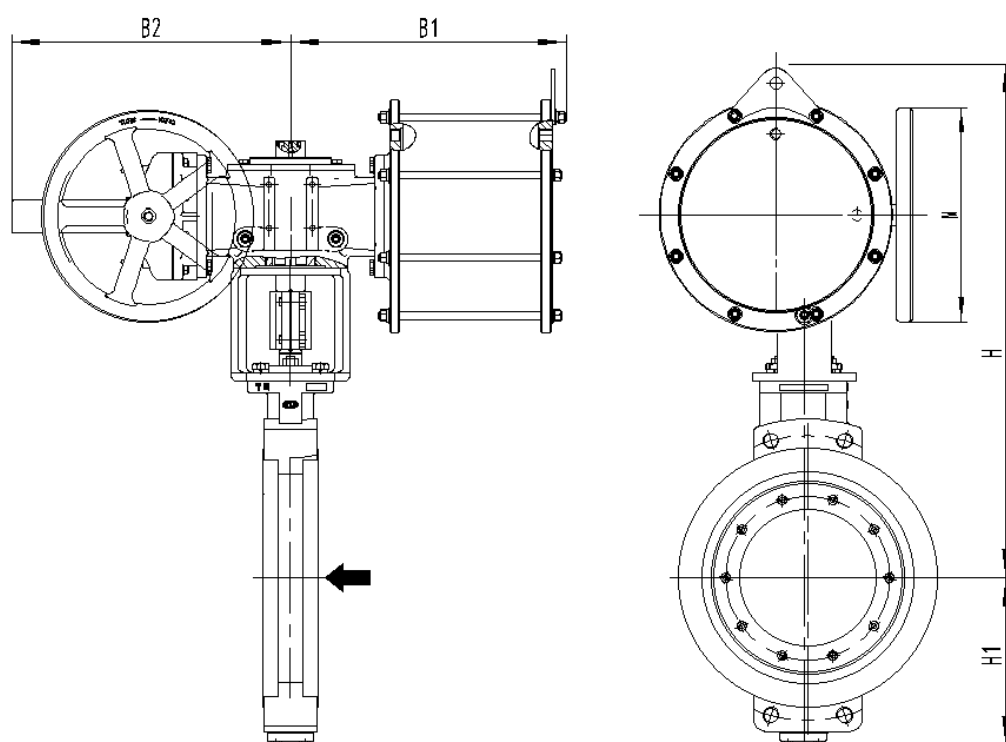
配 AW27D003~AW35D004 带伞齿手轮外形尺寸图
